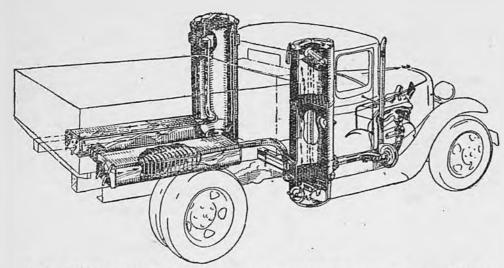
Расположение агрегатов газогенераторной установки НАТИ Г-14 на шасси автомобиля
